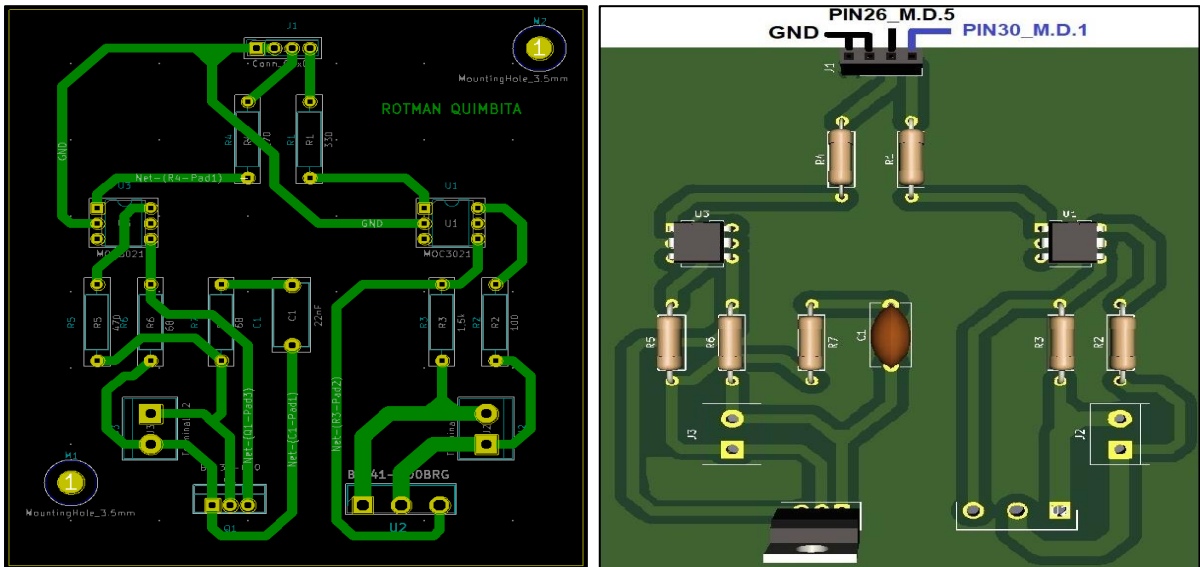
Módulo de disparo 1 y 5 - diseño PCB y visualización 3D.
